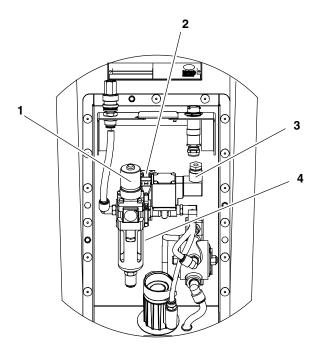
Komponenten Baugruppe Pneumatiksteuerung
